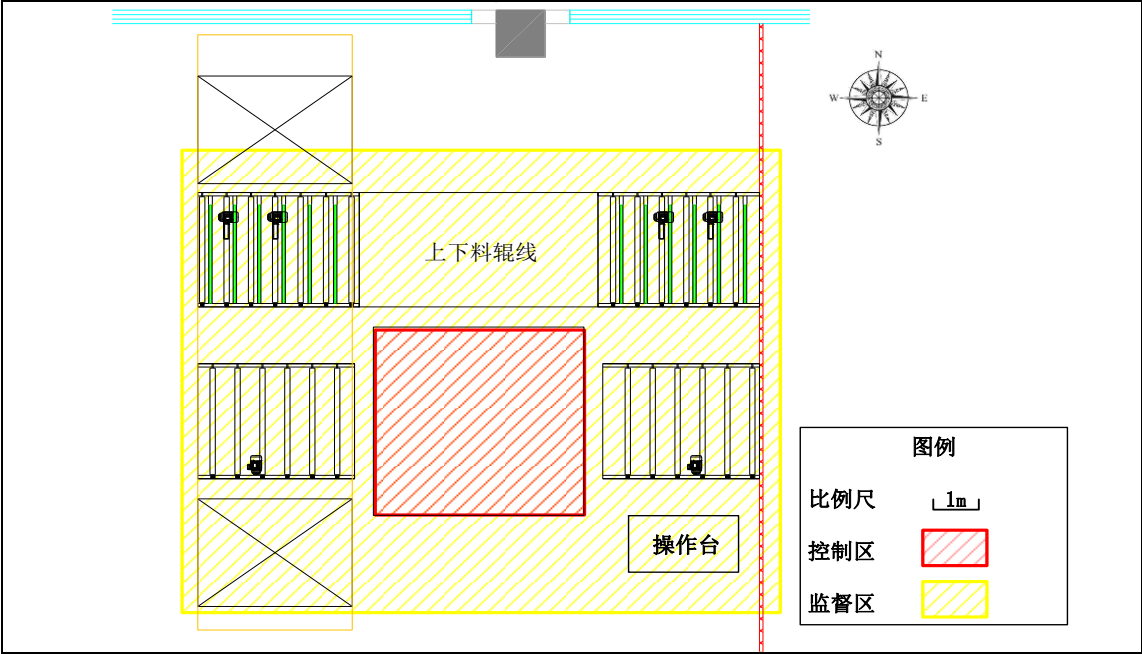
本项目X射线数字成像检测系统平面布置及分区示意图
